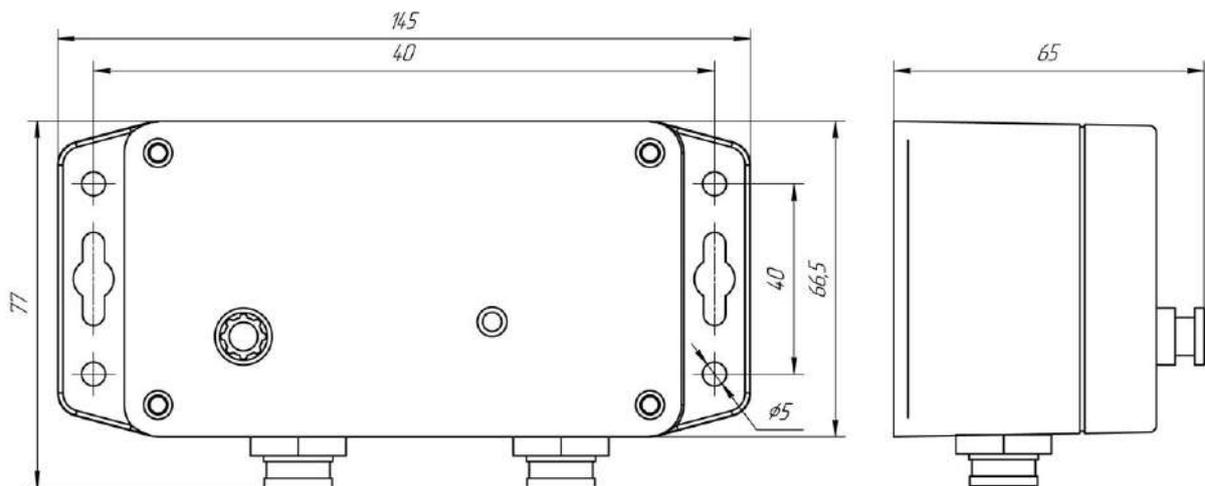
Габаритные и установочные размеры преобразователя питания ПП
